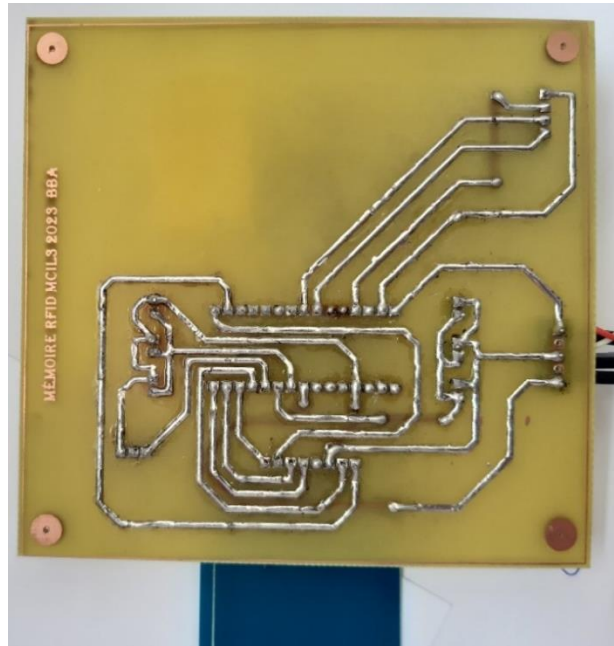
Soudage de différents composants dans le PCB imprimé
